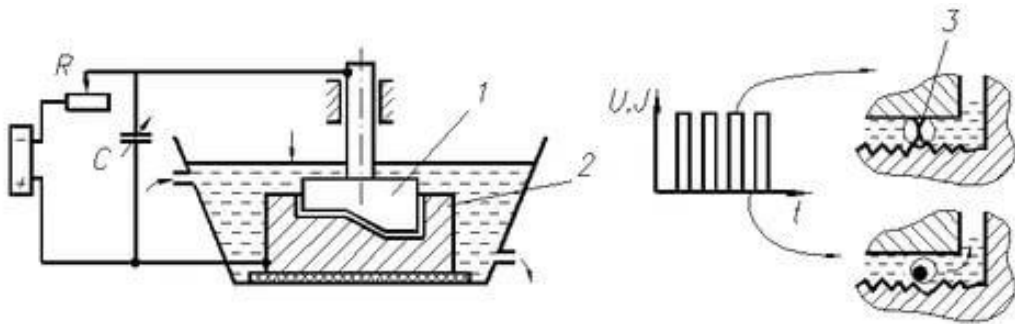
Схема установки для електроерозійної обробки: 1 – інструмент; 2 – деталь; 3 – проскакування іскри.
